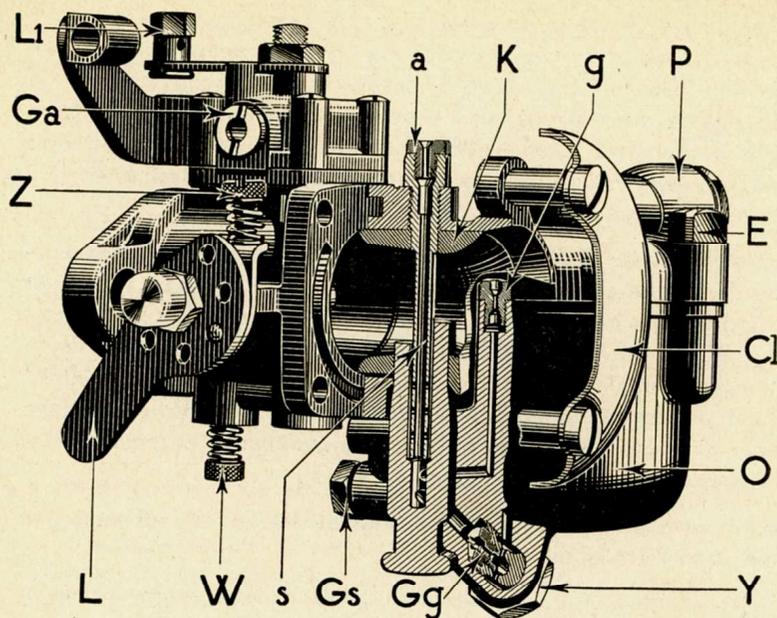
Coupe du carburateur horizontal (montage 22).
